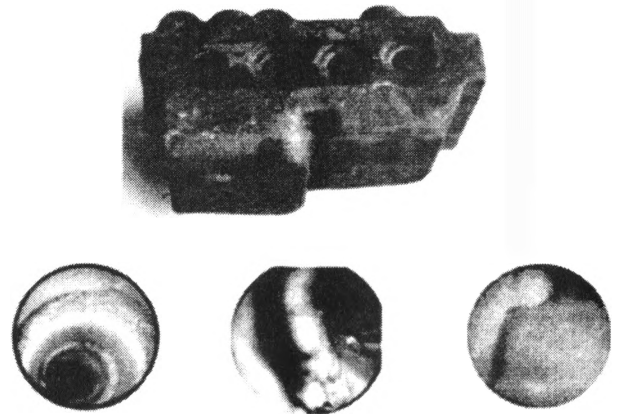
Отливка корпуса распределителя. Фотографии дефектных участков объектов контроля
